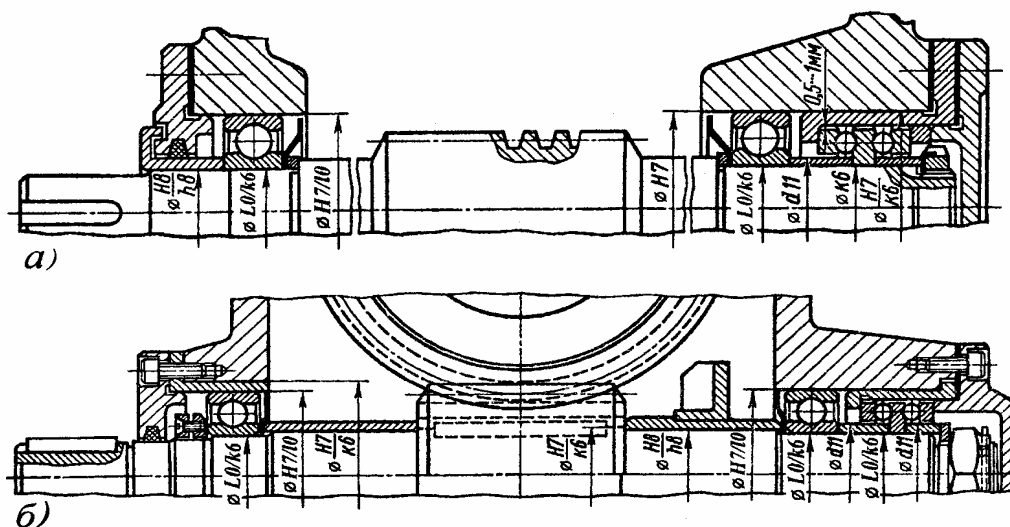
Конструкции фиксирующей опоры вала-червяка с радиальным и упорным подшипниками
